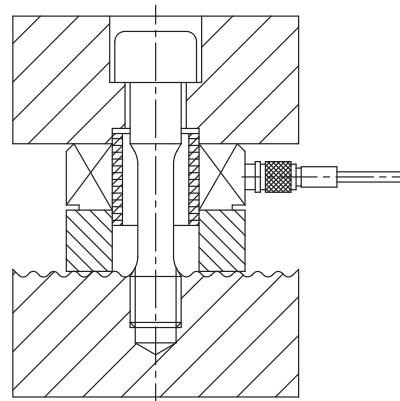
Einbau mit einem Druckverteilring Typ 9515 ... 9545
